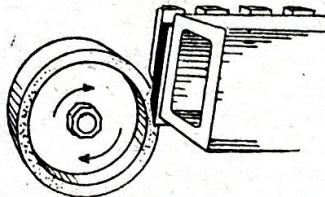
Неправильный способ закрепления ножа на держателе ножеточильного станка
